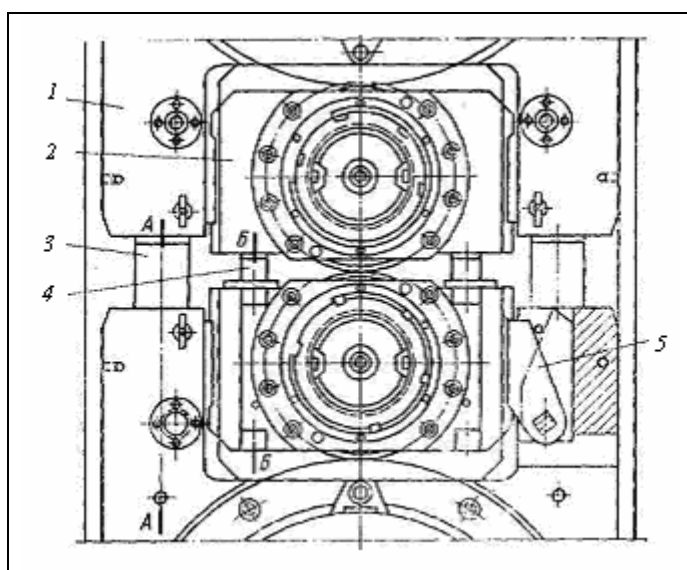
Рис. 7 Общий вид устройства для гидравлического уравнивания верхних рабочих и опорных валков четырех- валкового стана 1700 при помощи плунжеров между подушками валков:
